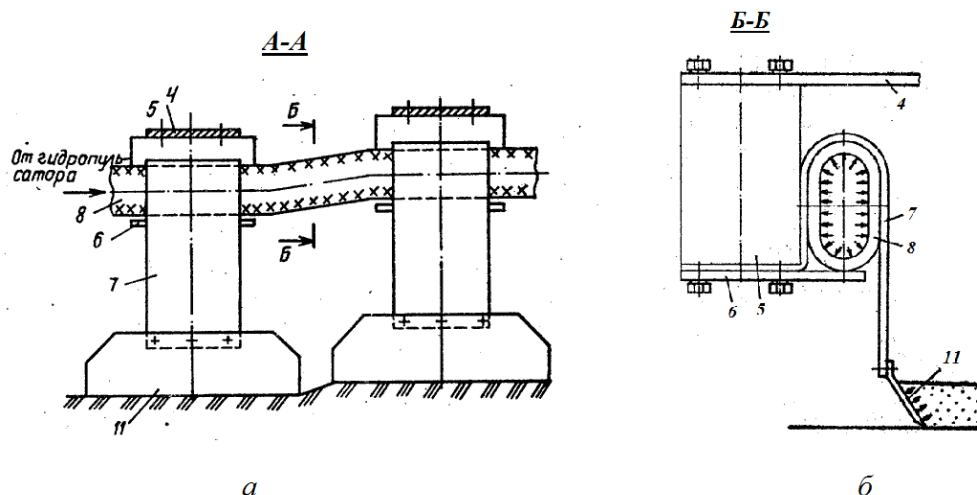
Рабочий орган вибрационного устройства для очистки дорожных покрытий от наледи в разрезе: а – разрез А-А; б – разрез Б-Б
